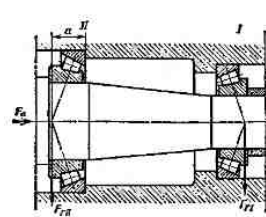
Схема установки конических роликоподшипников в ступице колеса
